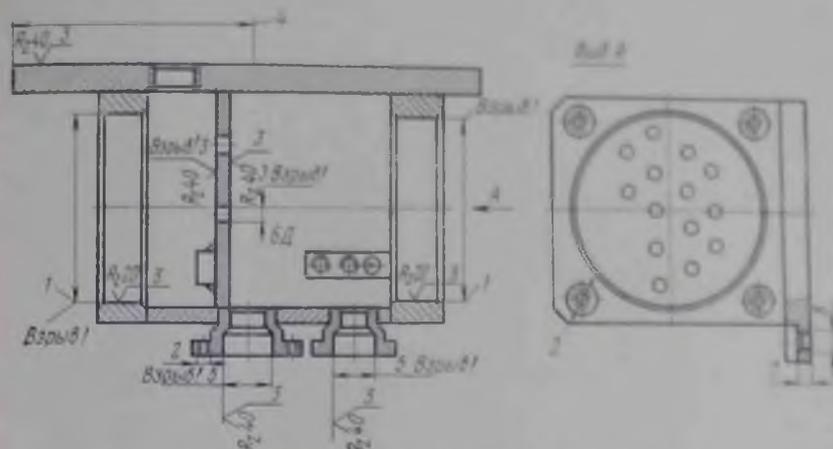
Взрывозащитный корпус комбайна 1К-101
